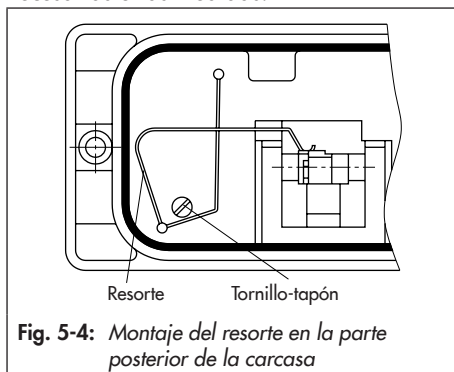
Montaje del resorte en la parte posterior de la carcasa
